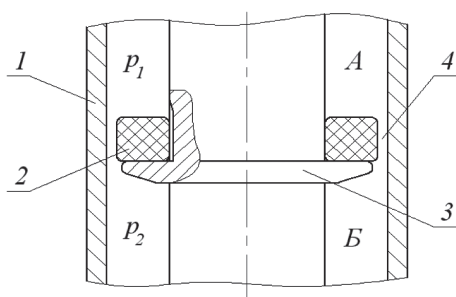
Схема клапанного устройства: 1 — цилиндр; 2 — упругий клапан; 3 — оправка; 4 — клапанная щель
